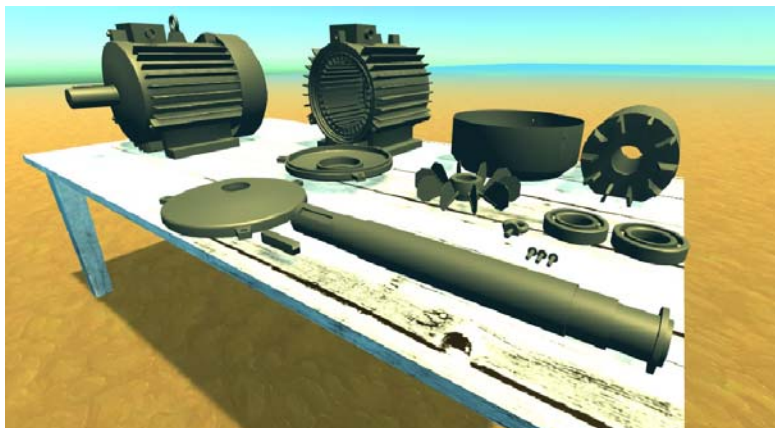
Вид основного блока по сборке-разборке асинхронного двигателя ремонтного цеха
